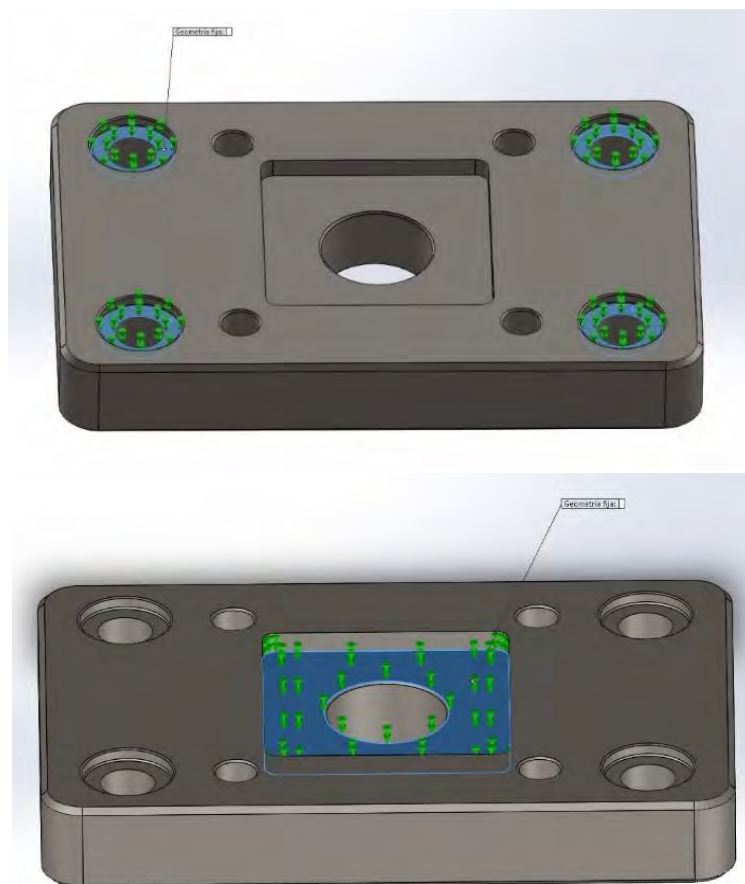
Distribución de geometrías fijas en la placa intermedia.
